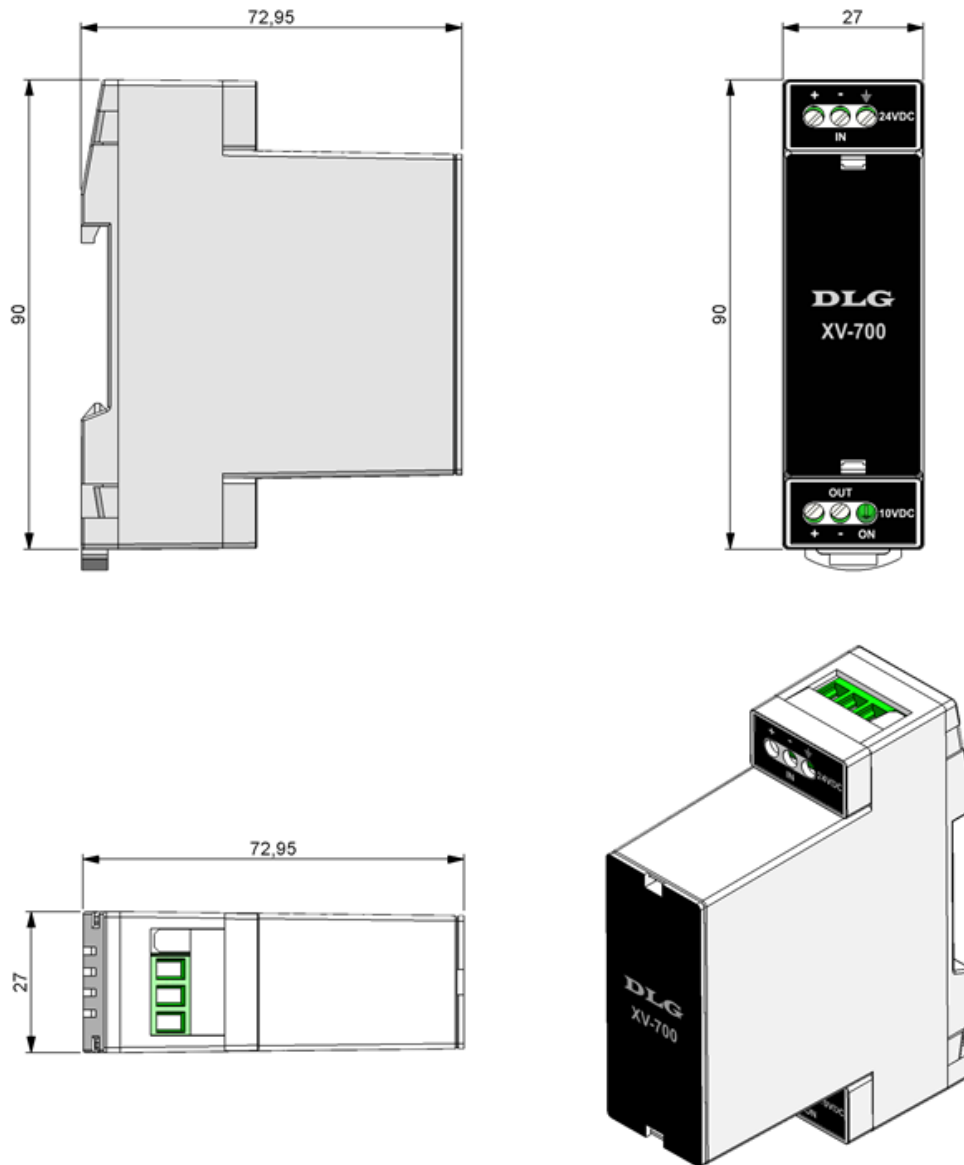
Dimensionamento para montagem (cotas em milímetros)
